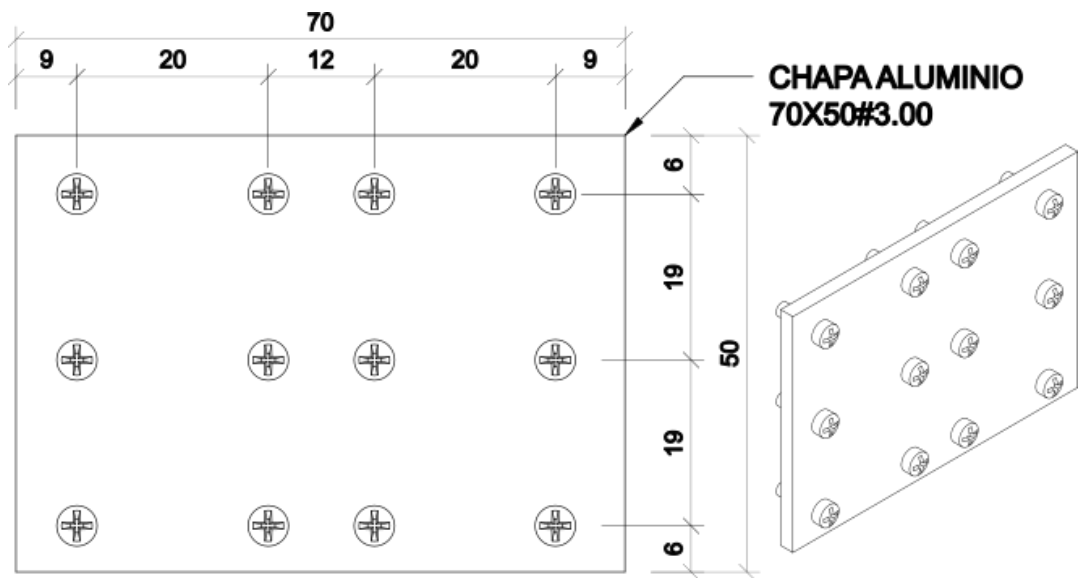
Detalhe da chapa de emenda e fixação das subestruturas.
